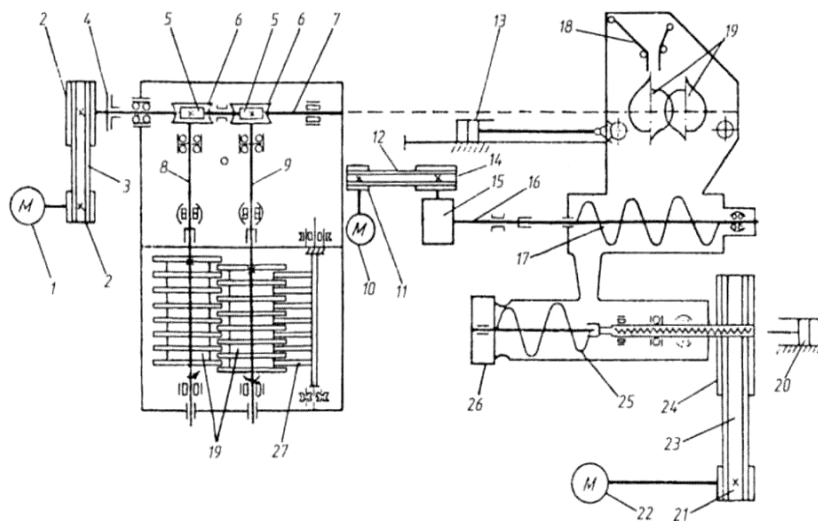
Кинематическая схема машины Я2-ФРР:
